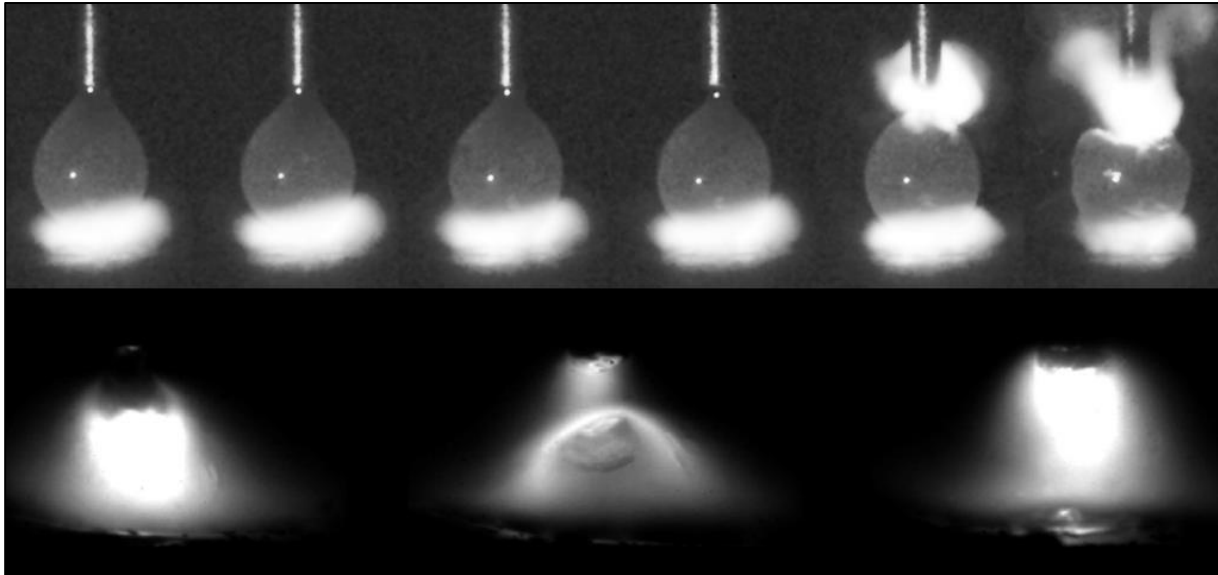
Ejemplos De Transferencia Globular En Soldadura [29 y 30].
